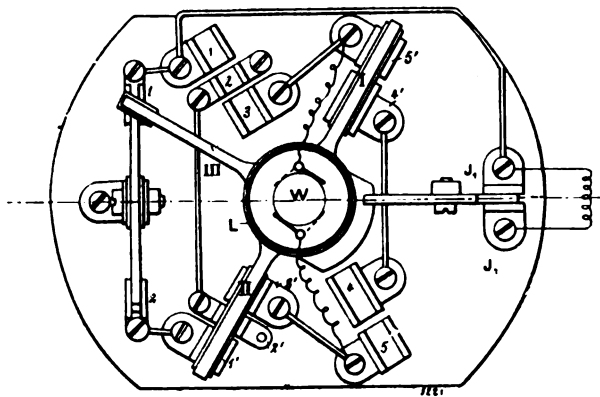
Vue en bout du plateau à connexions de la dynamo Stone.
